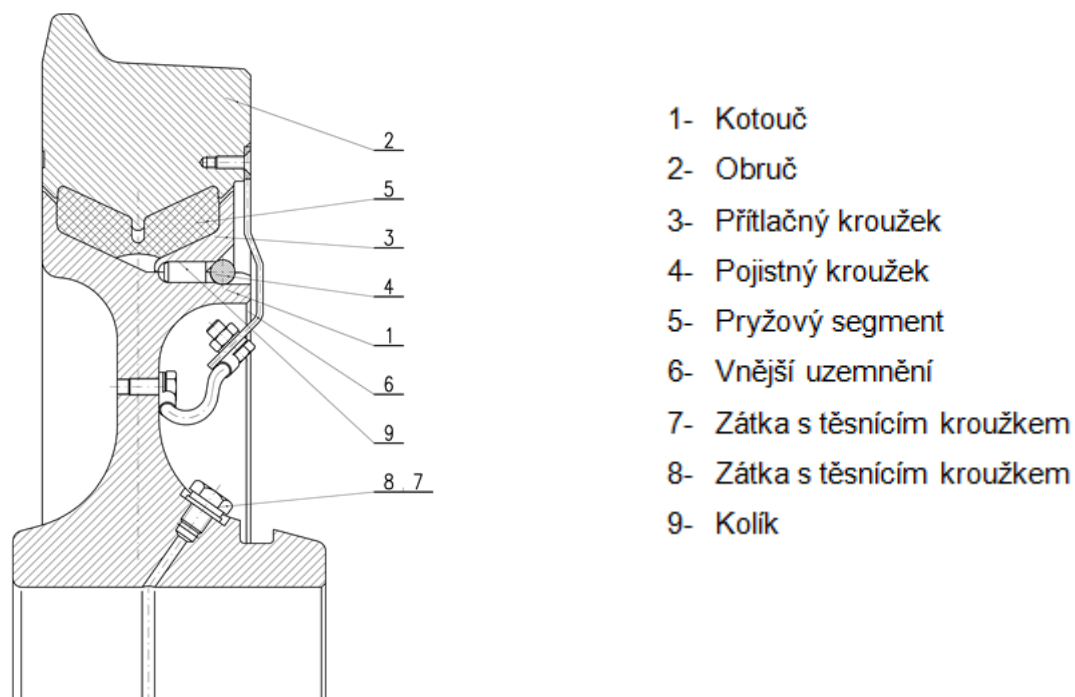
Půdorys konstrukčního řešení dvojkolí [5]
